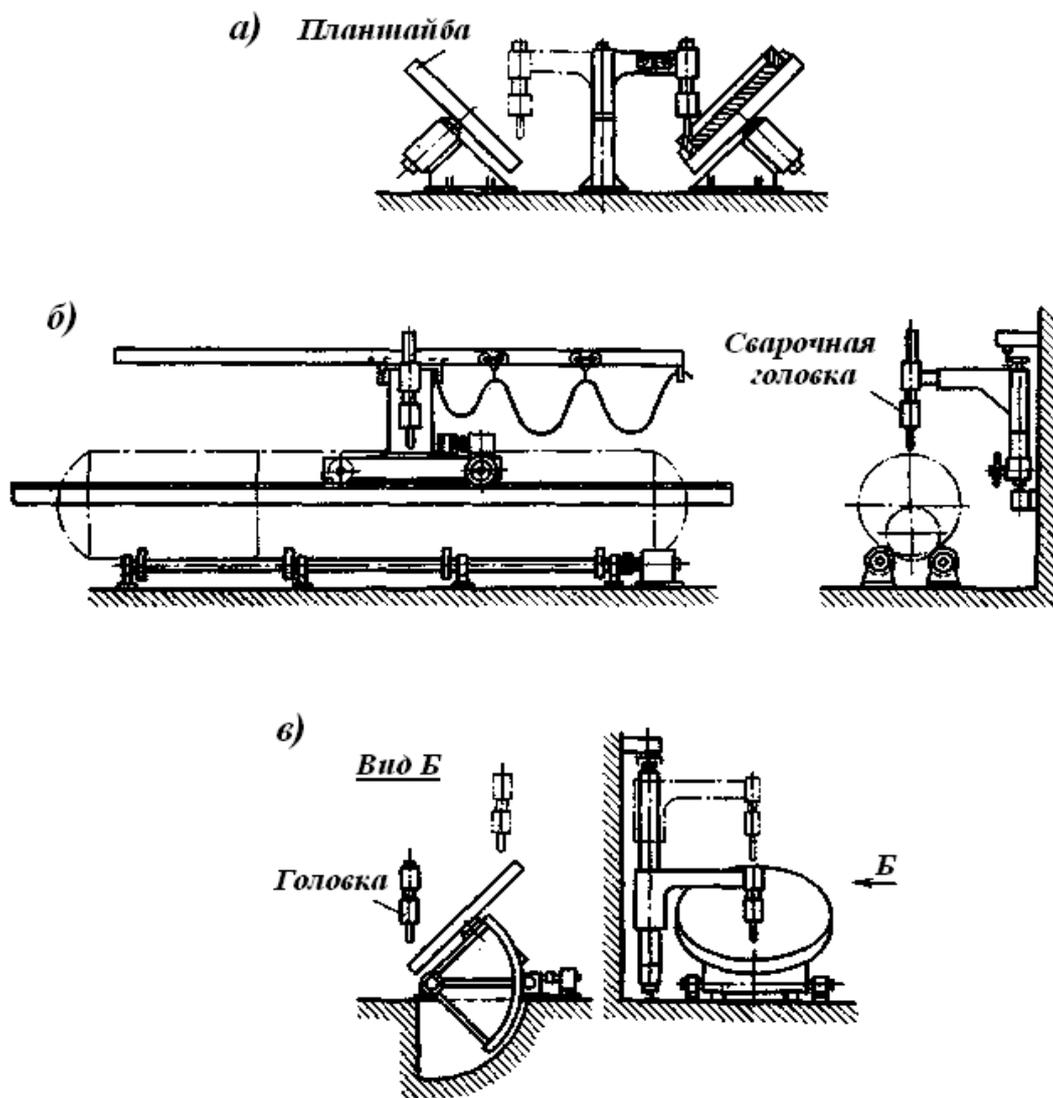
Основные типы сварочных приспособлений:
